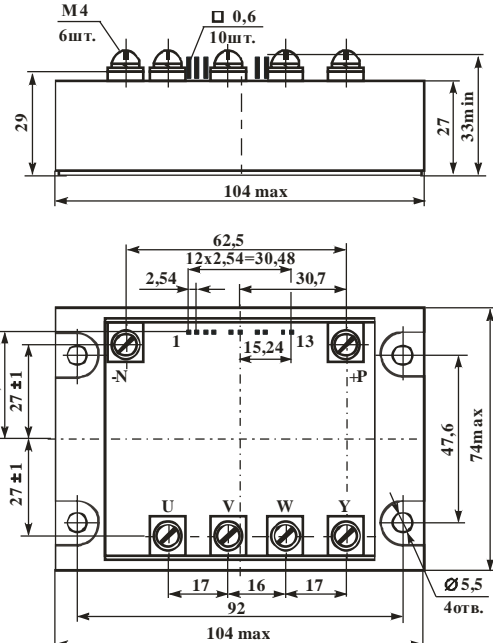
Габаритный чертеж модуля M13B-30-6; M13B-50-6
